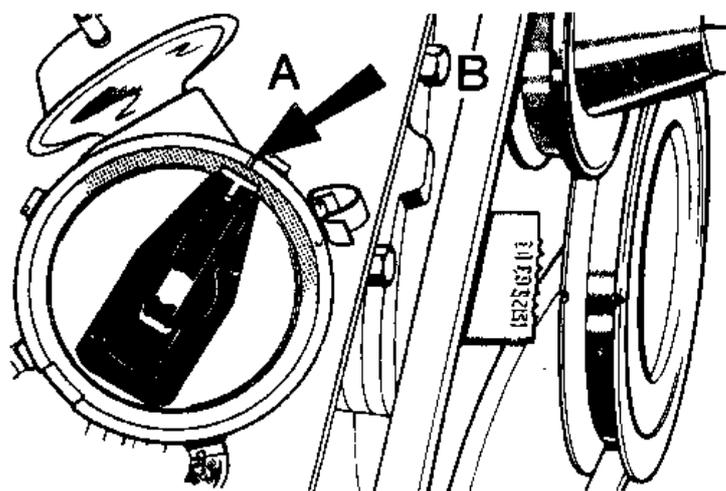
Двигатель установлен на 9° перед в.м.т. цилиндра №1 (Разд. 16)
